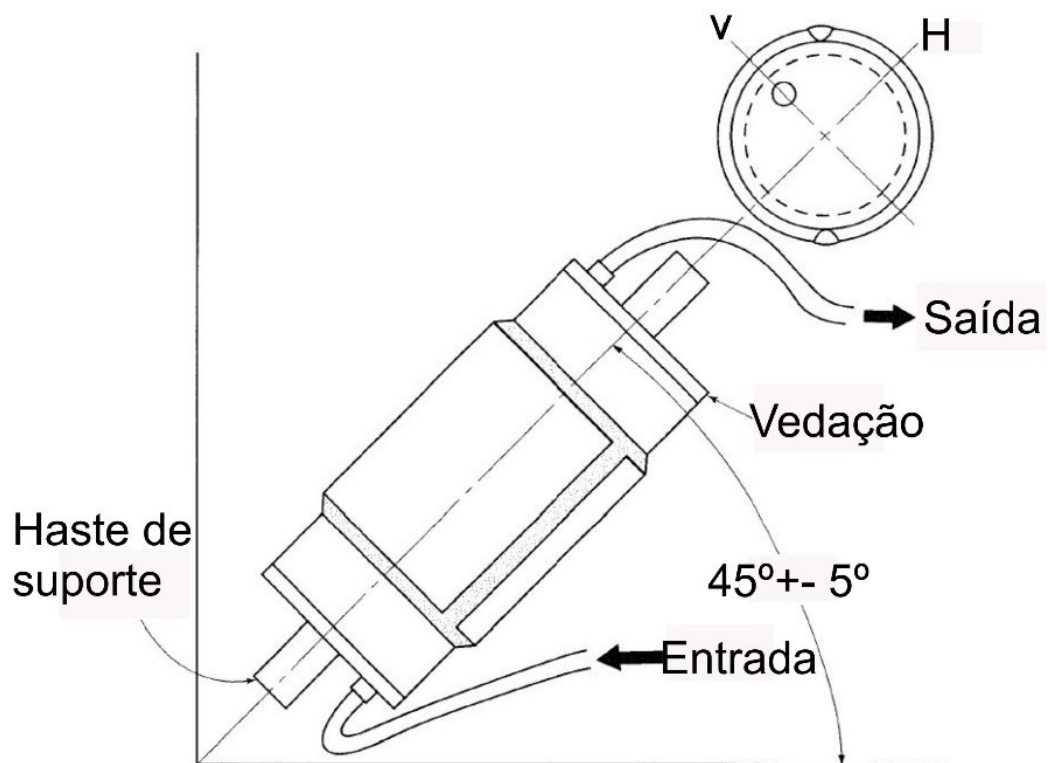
Esquema de bancada para qualificação do processo de soldagem para a norma API 1104
